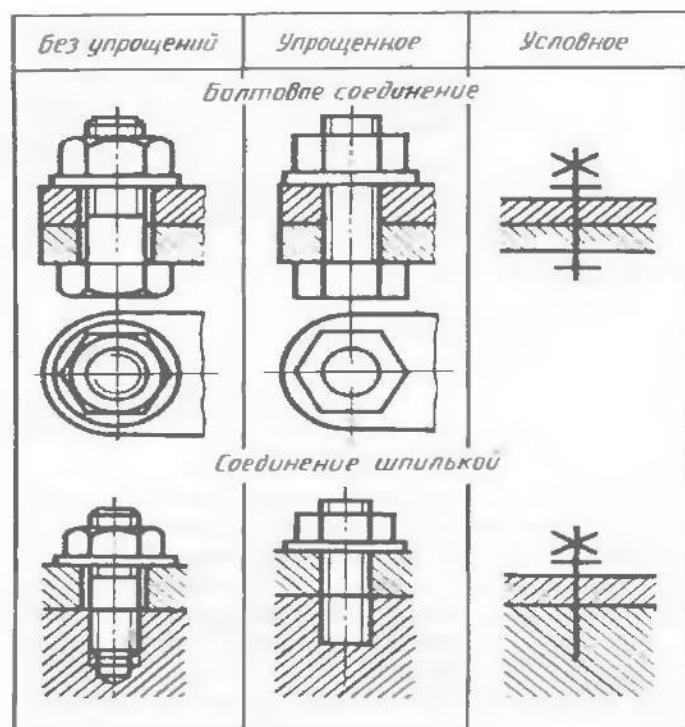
Резьбовое соединение болтом и шпилькой
